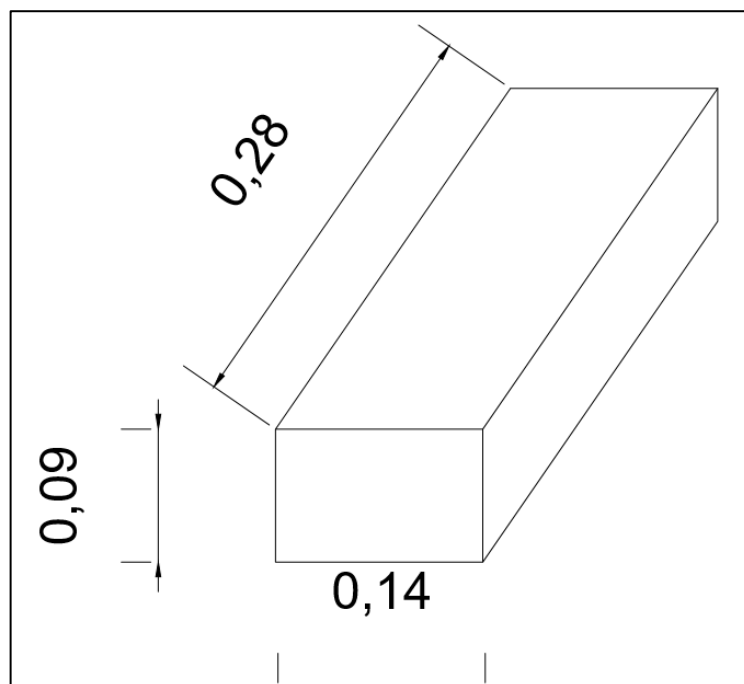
Dimensiones del molde para fabricar ladrillos artesanales.
